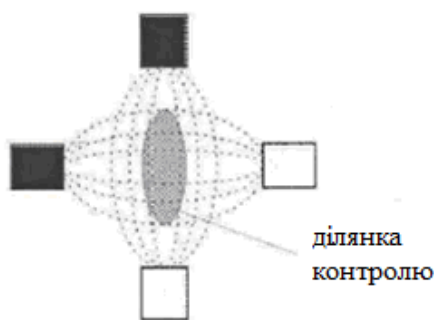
Схема намагнічування зон розчищення, обробки під зварювання та виправлення зварюванням
